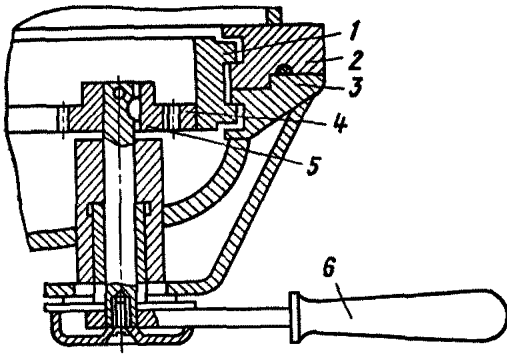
Соединение быстрооткрываемой крышки с корпусом
